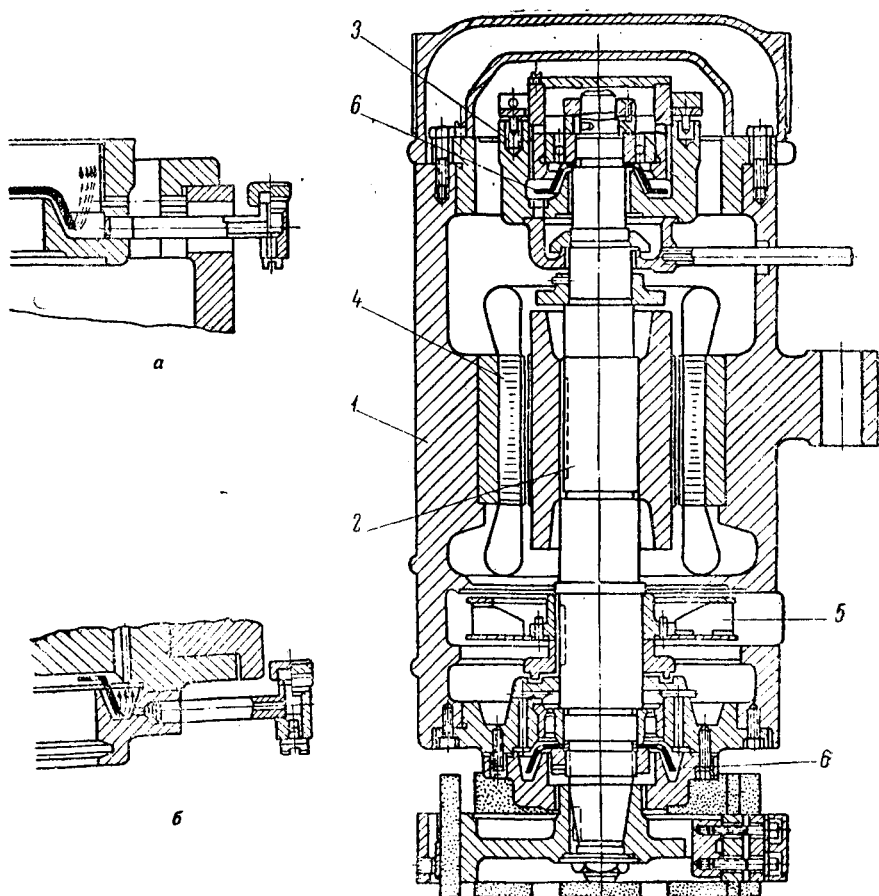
Шлифовальная бабка станка МСЗ, тип 3732
